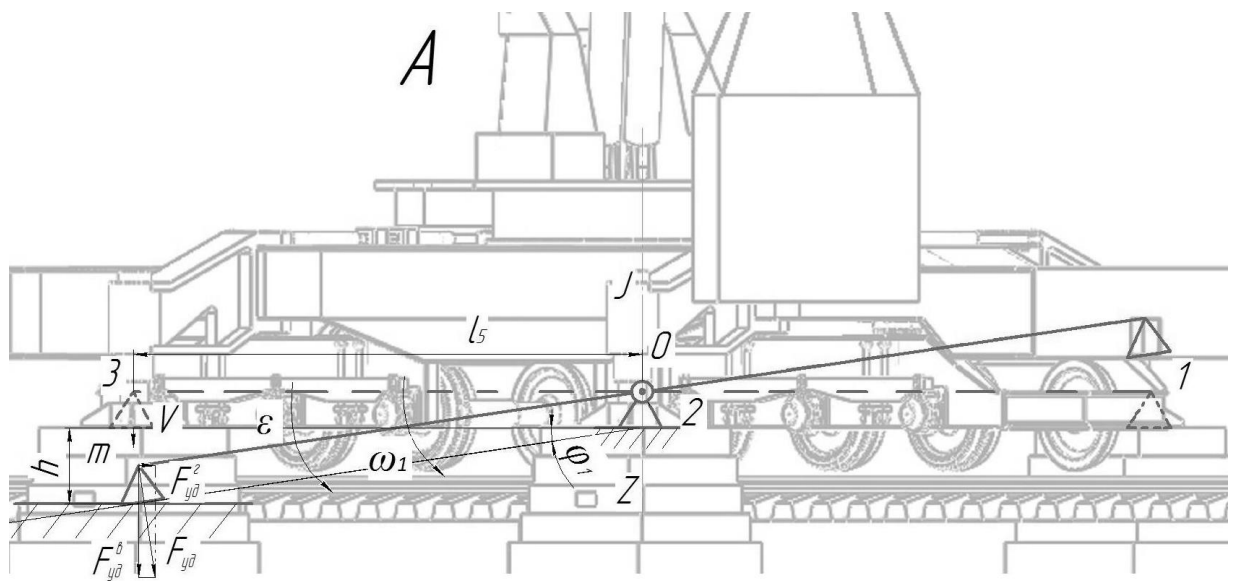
Расчетная схема для определения ударной нагрузки
